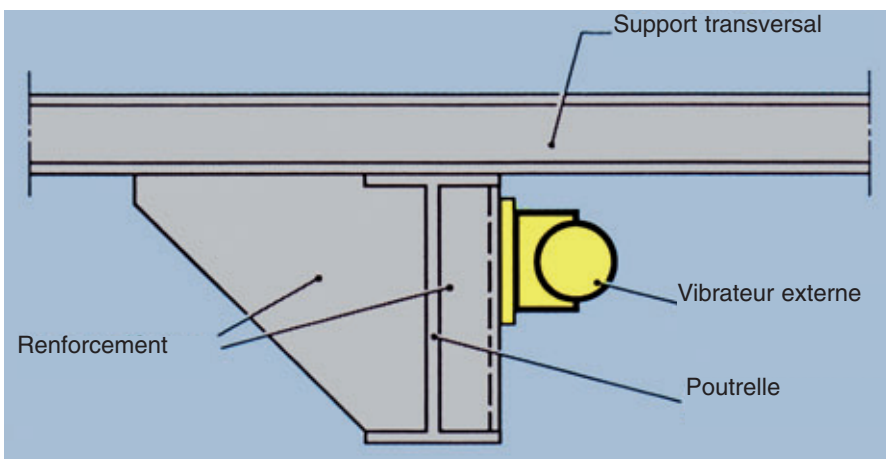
disposition du vibreur avec un renforcement au niveau de la poutrelle d'une grande table vibrante
